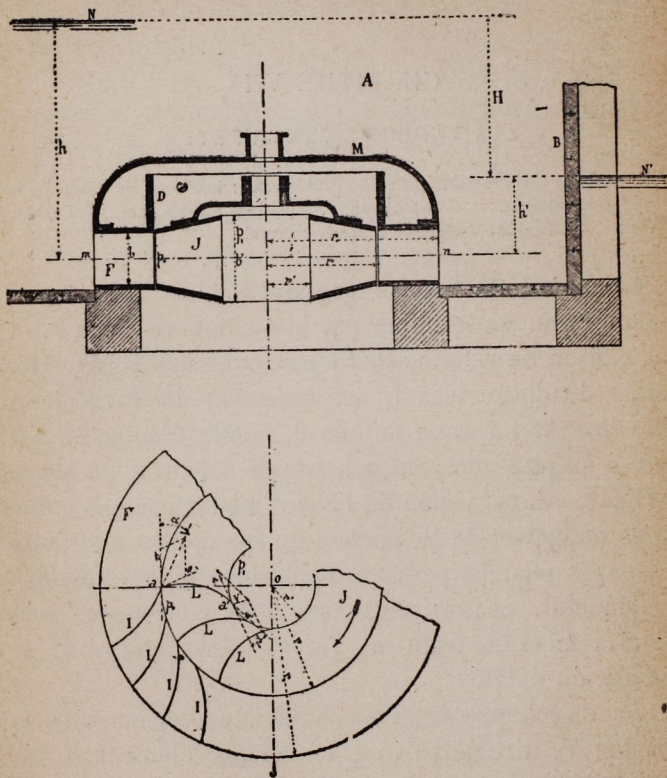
Principes de la turbine centripète, coupe verticale et coupe horizontale.
